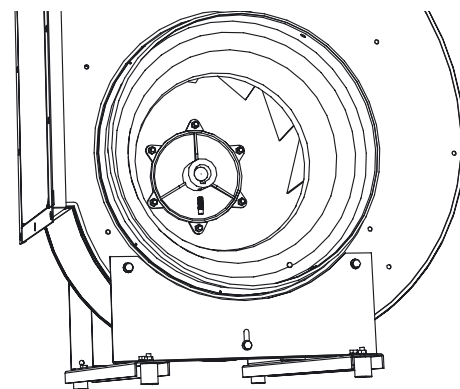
GTLB-1-022...071 Retirez la fixation du moyeu et la roue de l'arbre de moteur.
